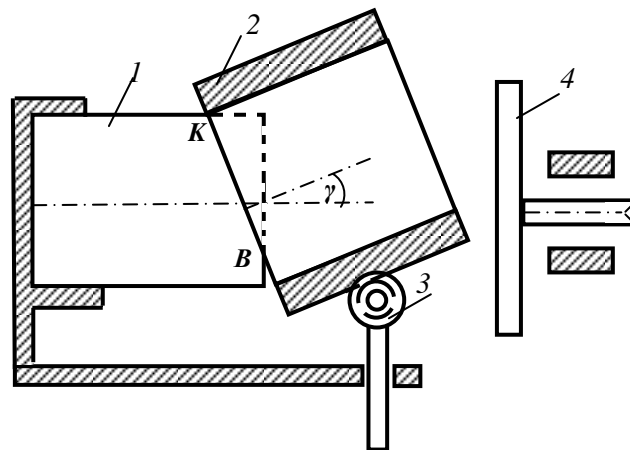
Способ сборки цилиндрических деталей в случае горизонтально закрепленного вала
